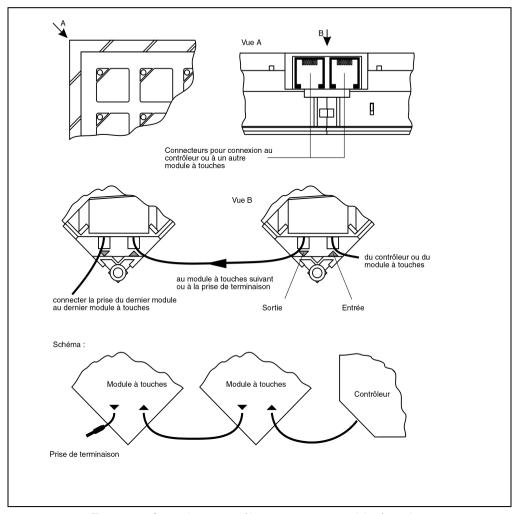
Connexion au contrôleur ou aux autres modules à touches
